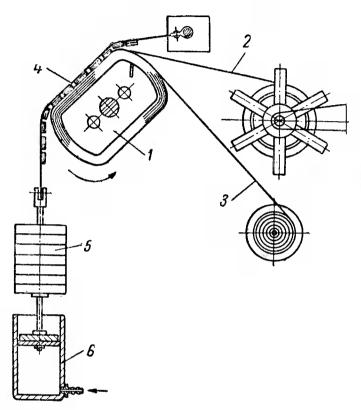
Станок для намотки овальных магнитопроводов трансформаторов типа ОСВ. 1—оправка; 2—стальная лента; 3—бумажная лента; 4—ленточный тормоз; 5—груз; 6—пневматический цилиндр.
